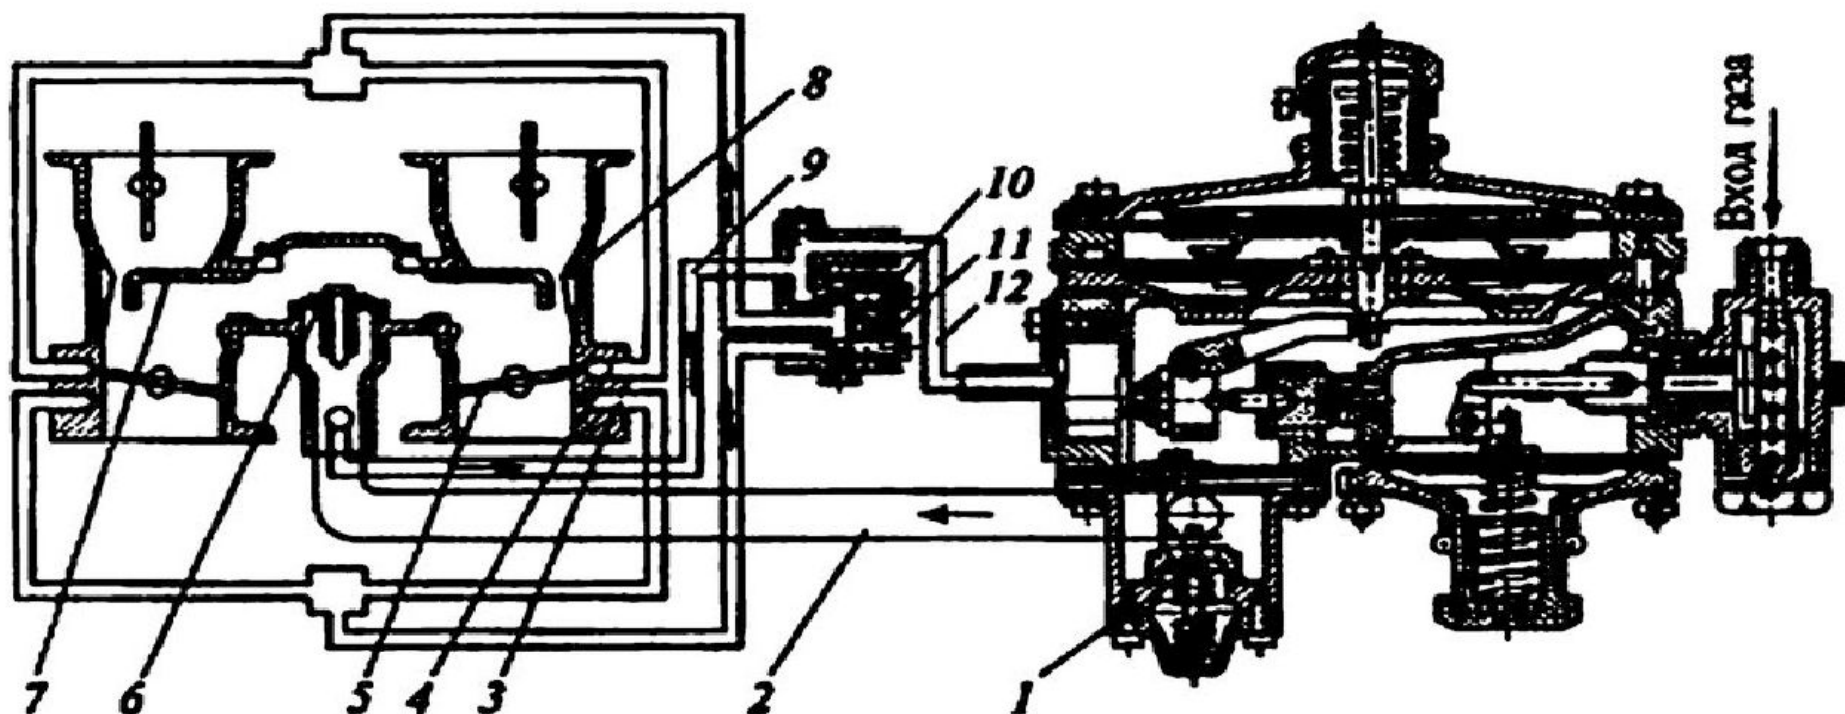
Схема соединения газового смесителя и двухступенчатого редуктора:
